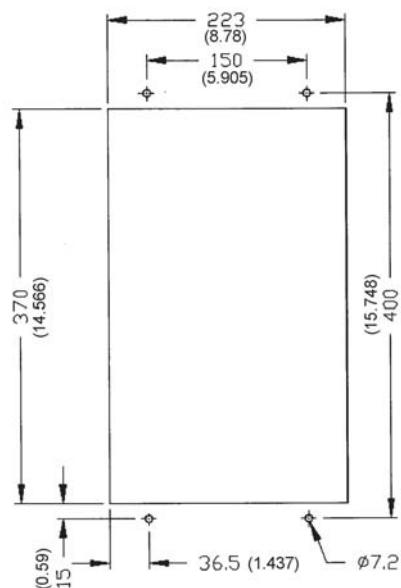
Dimensões do Rasgo para Montagem em Duto
